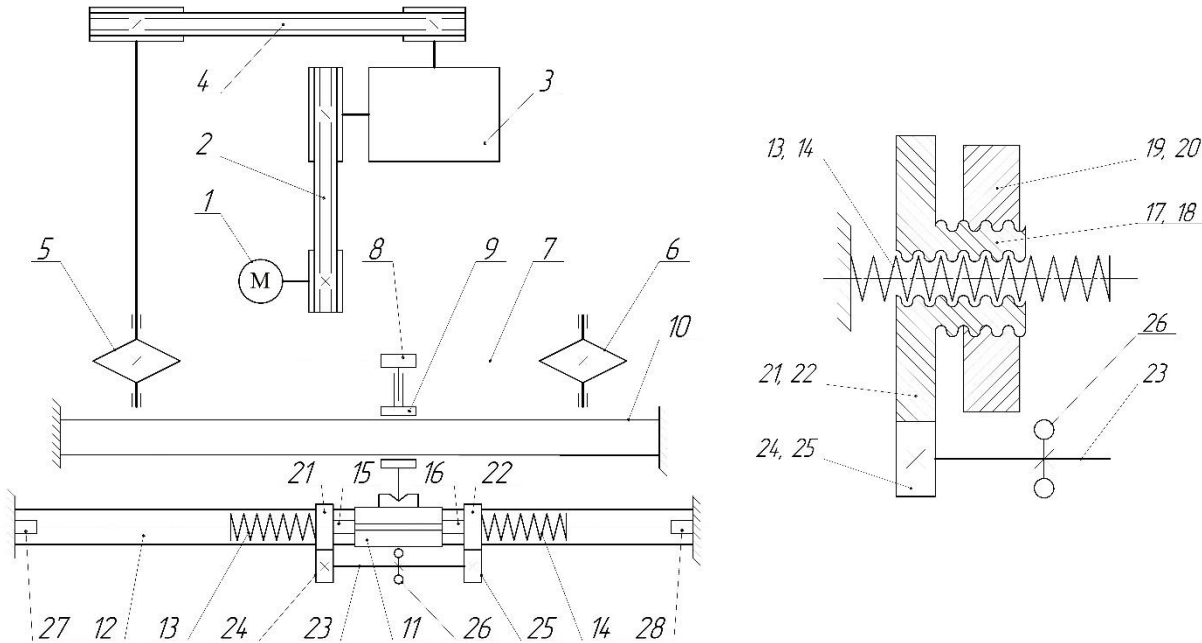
Кінематична схема приводу рукавичного автомата: 1 – електродвигун; 2, 4 – клинопасові передачі; 3 – редуктор; 5 – ведуча зірочка ланцюгової передачі; 6 – ведена зірочка ланцюгової передачі; 7 – тяговий ланцюг; 8 – палець; 9 – проміжна каретка; 10, 12 – напрямні; 11 – в'язальна каретка; 13, 14 – пружини стиску; 15, 16 – пристрої регулювання жорсткості пружин стиску; 17, 18 – втулки; 19, 20 – нерухомі гайки; 21, 22 – зубчасті колеса; 23 – вал; 24, 25 – шестерні; 26 – маховик; 27, 28 – упори
